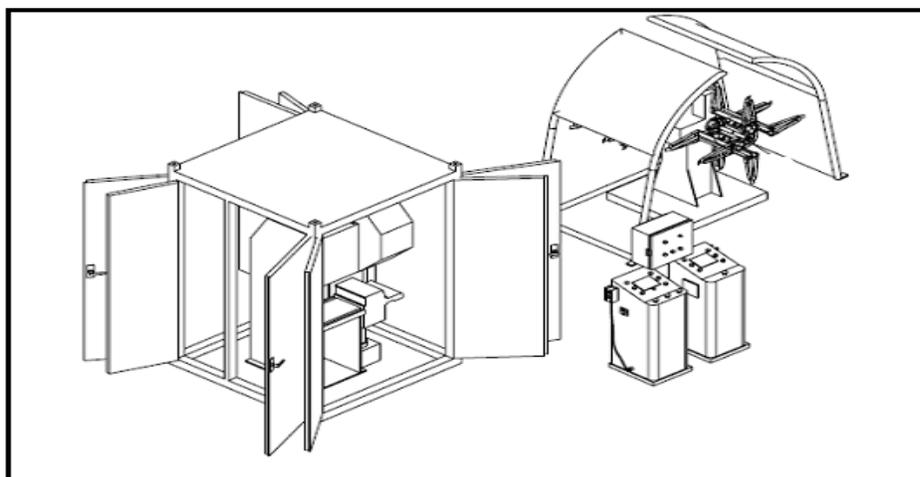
Localização esquemática dos subconjuntos do equipamento piloto.
